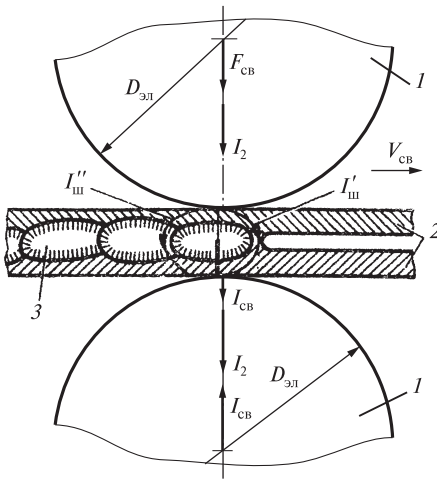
Схема шовной сварки: 1 — электрод; 2 — свариваемые детали; 3 — шовное соединение; $V_{св}$ — скорость сварки; I_2 — вторичный ток; $I'_ш$, $I''_ш$ — токи шунтирования
